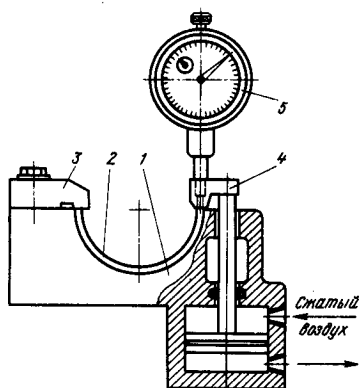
Схема контроля выступающего вкладыша по высоте: 1 — гнездо; 2 — вкладыш; 3 — жесткий упор; 4 — пружин; 5 — индикатор
